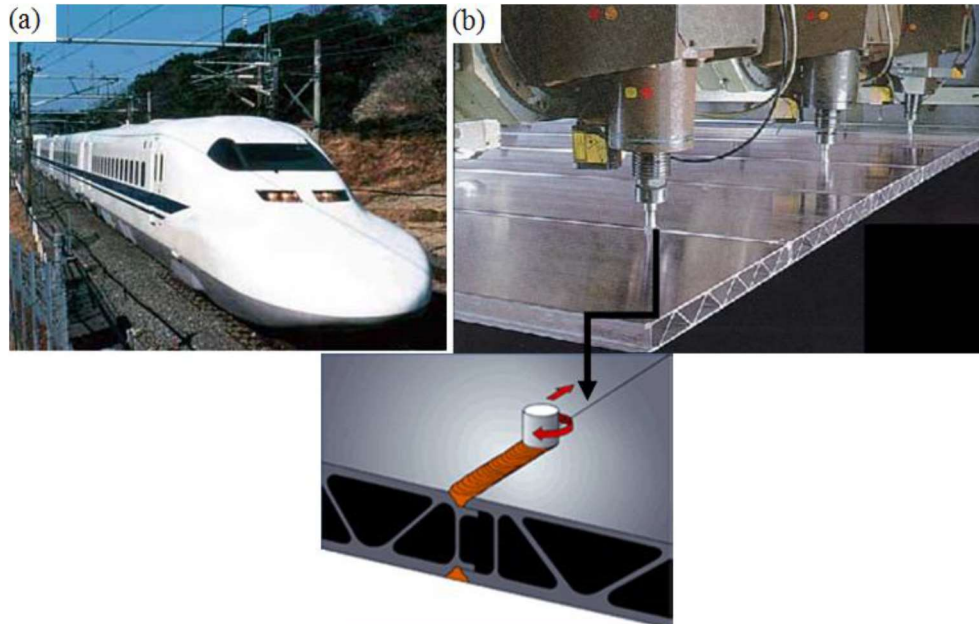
Soudage par FSW trains : (a) Hitachi train Série 700, (b) Technique de soudage des carrosseries des trains Hitachi [1].
